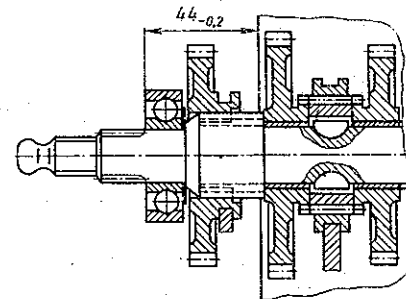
Montage du roulement arrière de l'arbre secondaire
